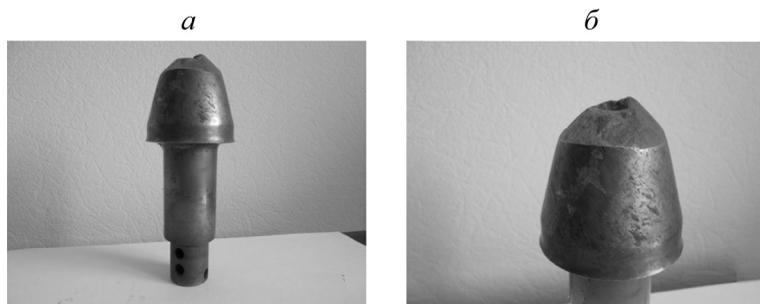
Изношенный комбайновый резец (а) и его головка (б)
